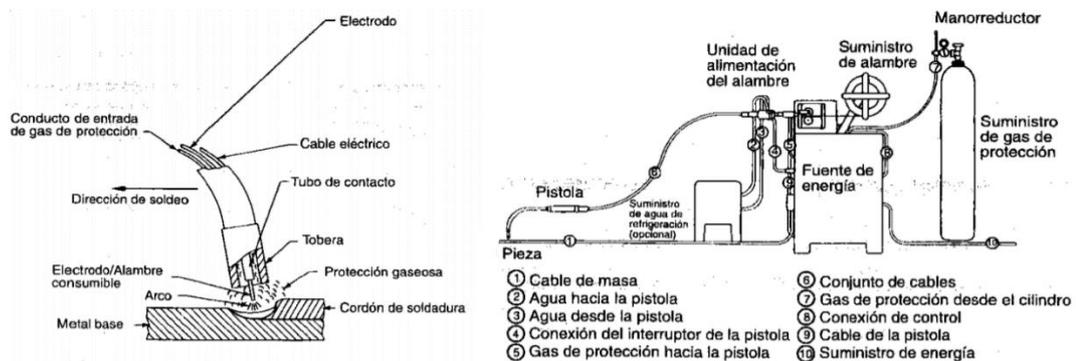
Soldadura por arco con gas de protección y equipo de soldado. Fuente: LincolnElectric
